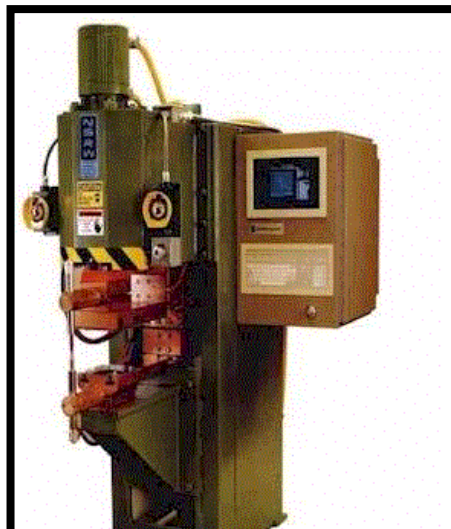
FOTO DE UNA SOLDADURA DE PUNTO
